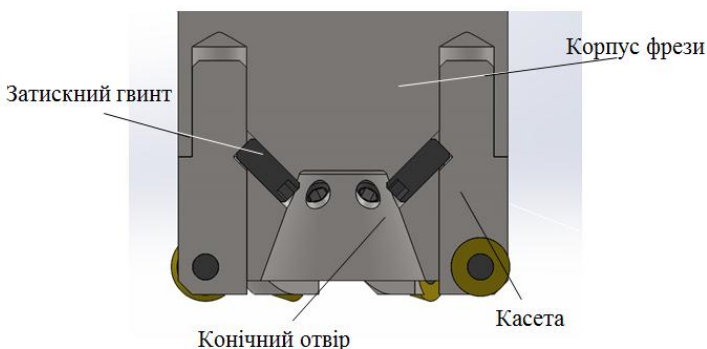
Удосконалений метод закріплення касети у корпусі фрези
